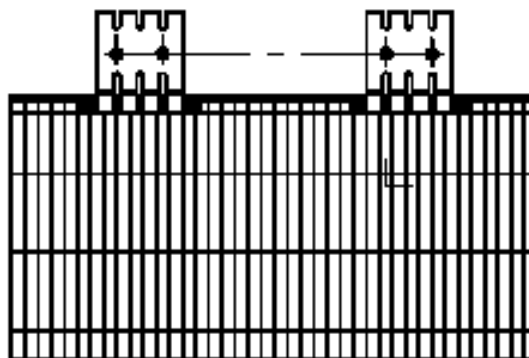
Interconectores soldados a uma célula solar. Extraída de [7].
